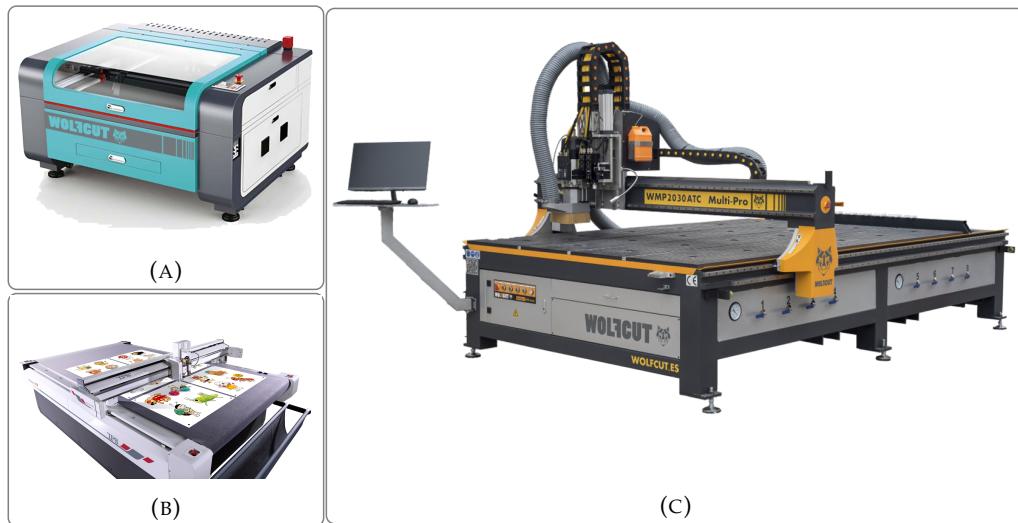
Maquinas CNC fabricadas por la empresa Wolfcut.
